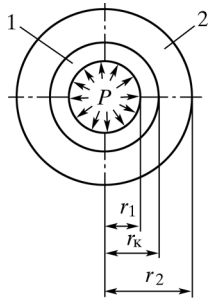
Схема нагружения двухслойной трубы: 1, 2 — трубы
